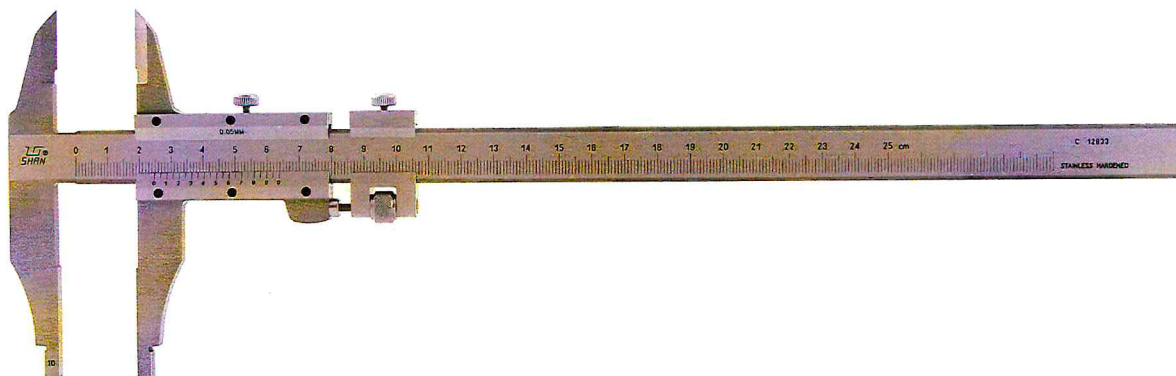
Общий вид штангенциркулей двусторонних без глубиномера с отсчетом по нониусу
